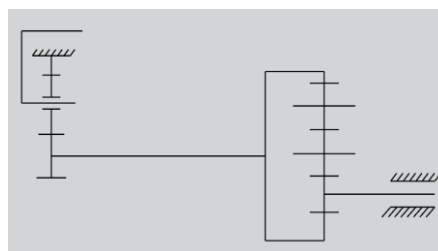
Кинематическая схема двухступенчатого несоосного колесного редуктора
